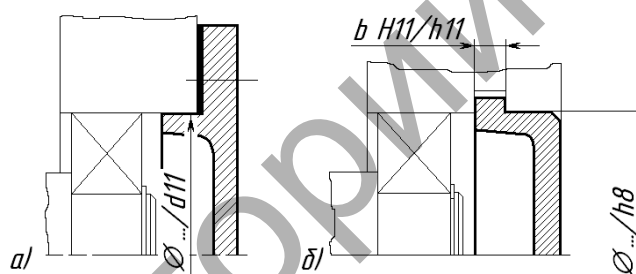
Закрепляемая винтами и закладная крышки без отверстия для прохода вала
